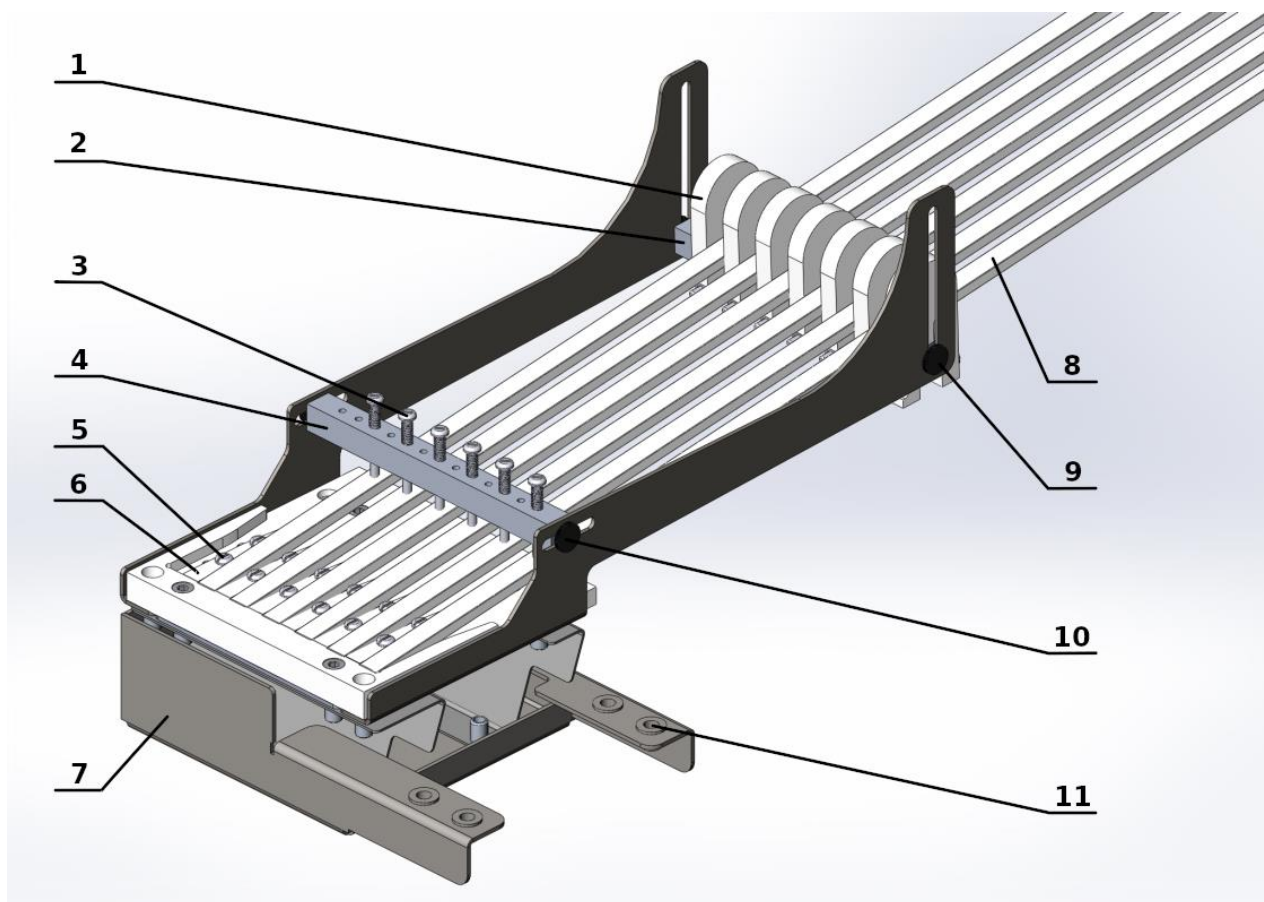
Приспособление для обрезки верхней части пенала
